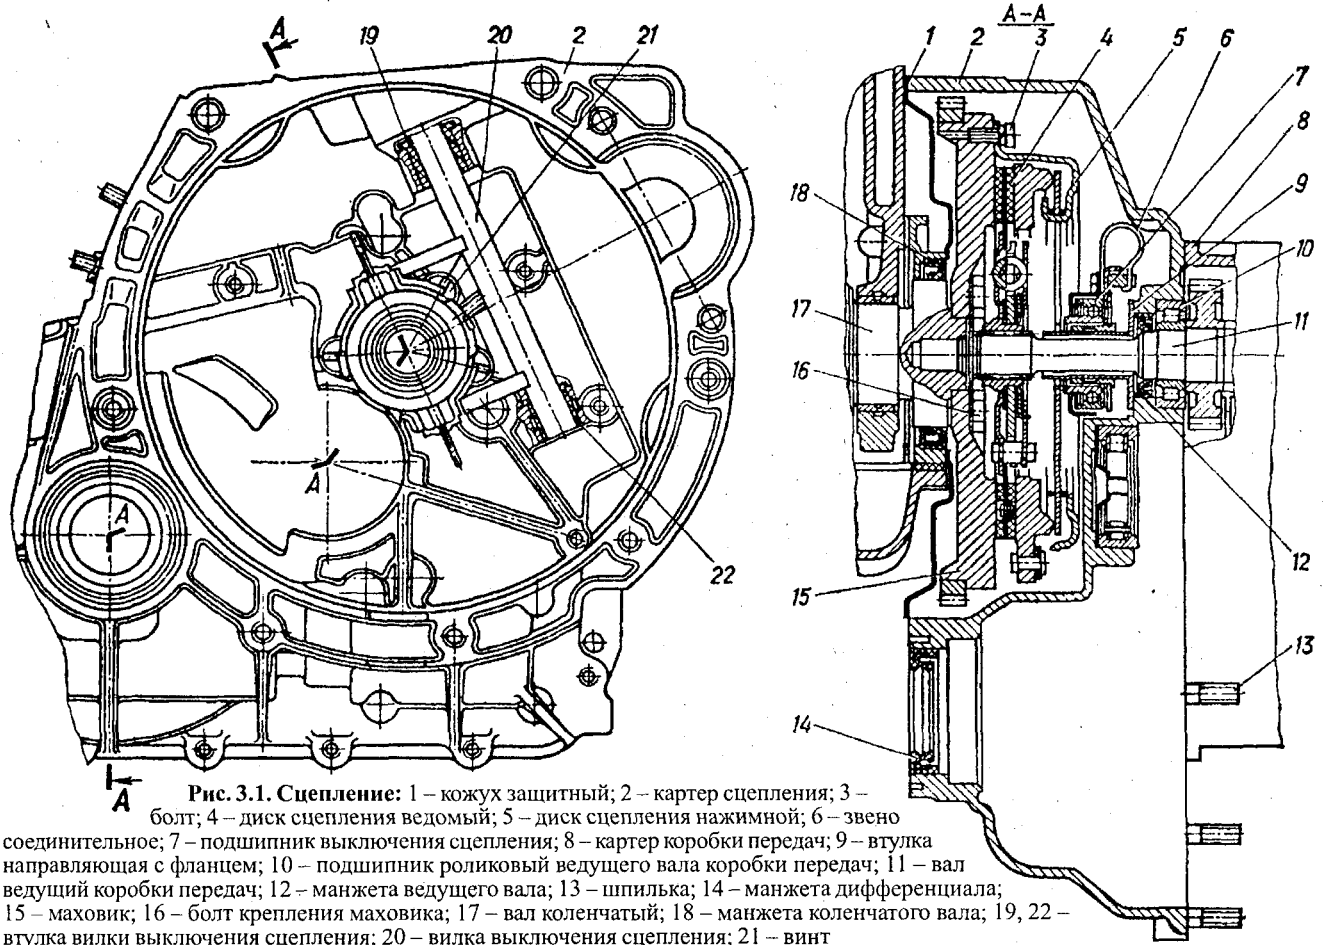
Сцепление: 1 – кожух защитный; 2 – картер сцепления; 3 – болт; 4 – диск сцепления ведомый; 5 – диск сцепления нажимной; 6 – звено соединительное; 7 – подшипник выключения сцепления; 8 – картер коробки передач; 9 – втулка направляющая с фланцем; 10 – подшипник роликовый ведущего вала коробки передач; 11 – вал ведущий коробки передач; 12 – манжета ведущего вала; 13 – шпилька; 14 – манжета дифференциала; 15 – маховик; 16 – болт крепления маховика; 17 – вал коленчатый; 18 – манжета коленчатого вала; 19, 22 – втулка вилки выключения сцепления; 20 – вилка выключения сцепления; 21 – винт
